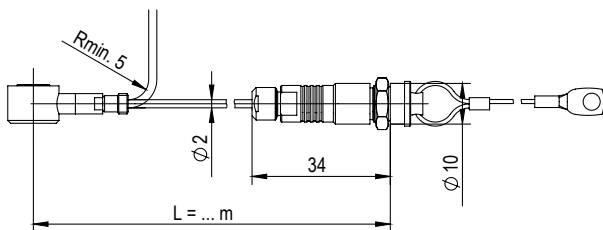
Kraftsensor Typ 9204B 0,2/0,4/0,6/0,8/sp mit Kabel und Stecker
